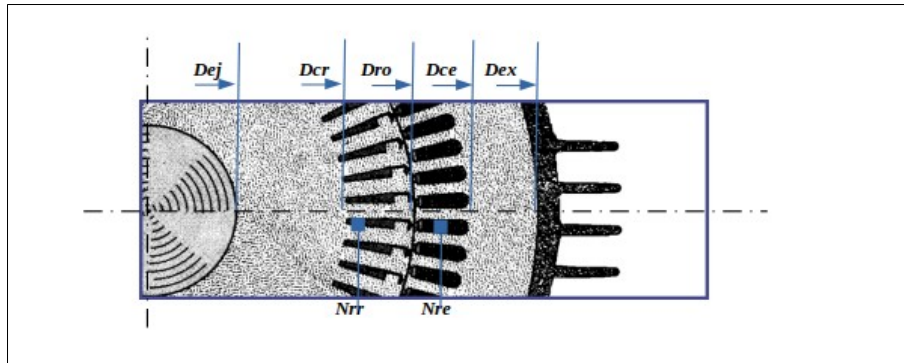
DER. Dimensiones del estator y rotor (DER)
